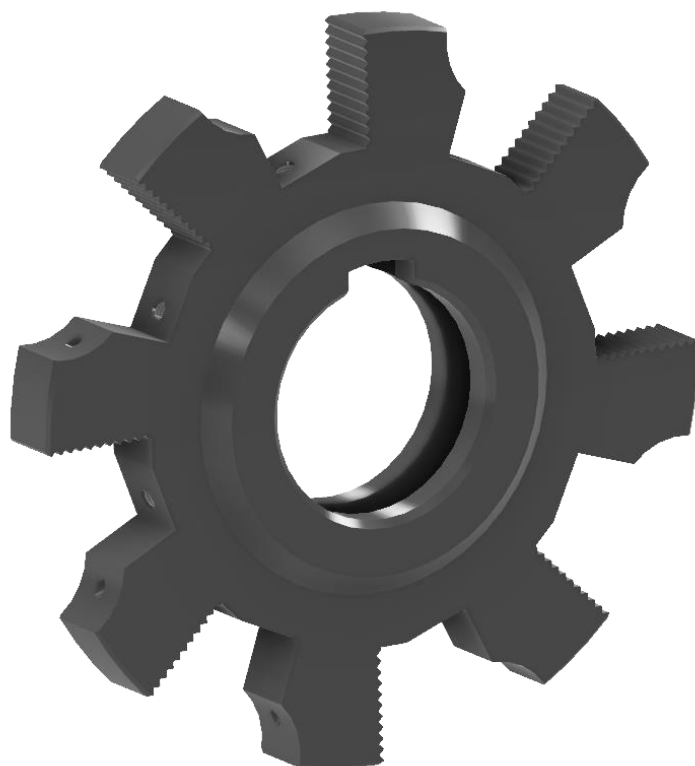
Зовнішній вигляд корпусу фрези дискової збірної для оброблення пазів
